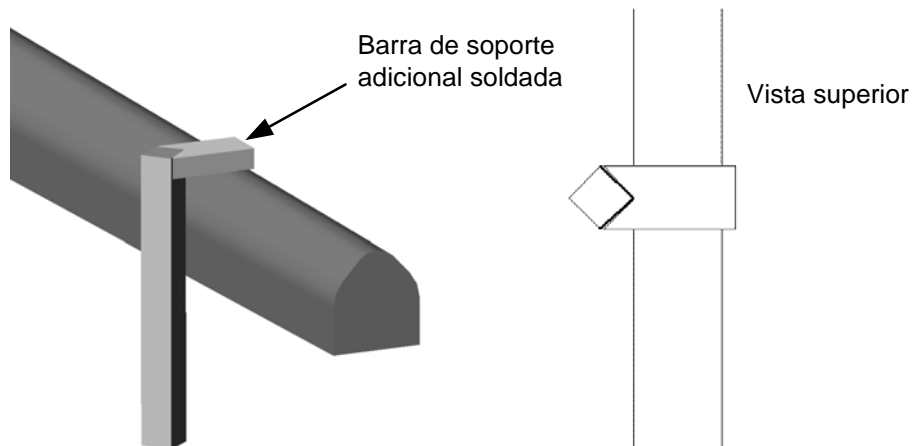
Barra de montaje cuadrada soldada al brazo de la pala del raspador
